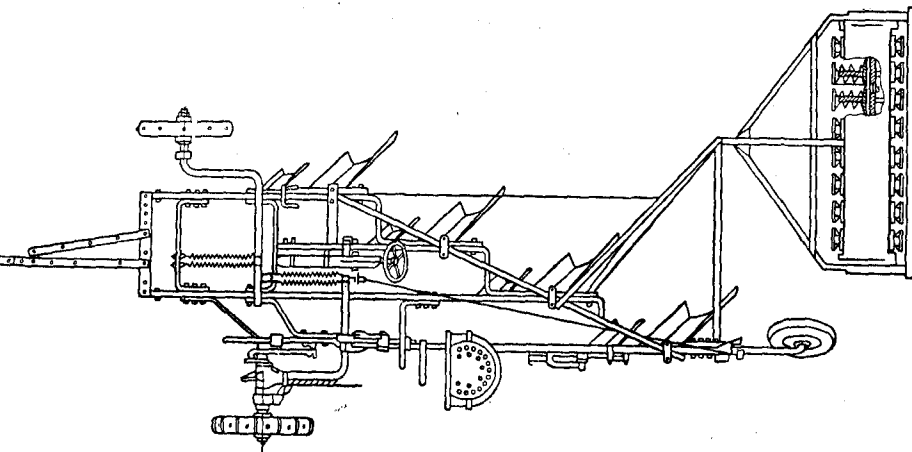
Комбинированный пахотный агрегат АПК-1,75
